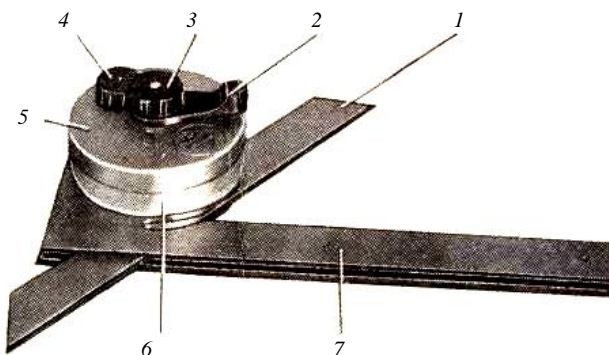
Оптический угломер: 1 – подвижная линейка; 2 – зажимной рычаг; 3 – зажимной винт; 4 – окуляр; 5 – крышка; 6 – корпус; 7 – основание
